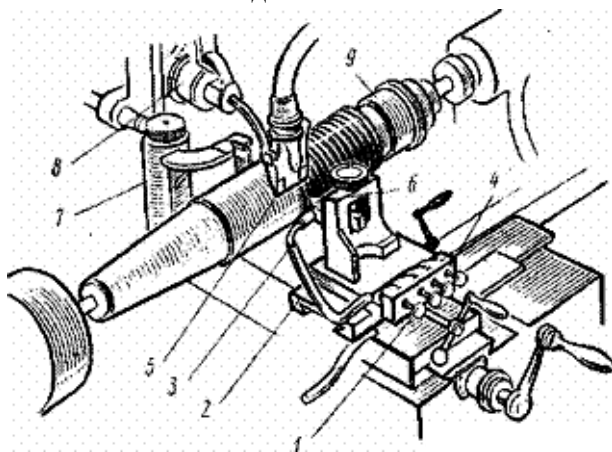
Схема установки для наплавки под слоем флюса с принудительным охлаждением деталей водой
